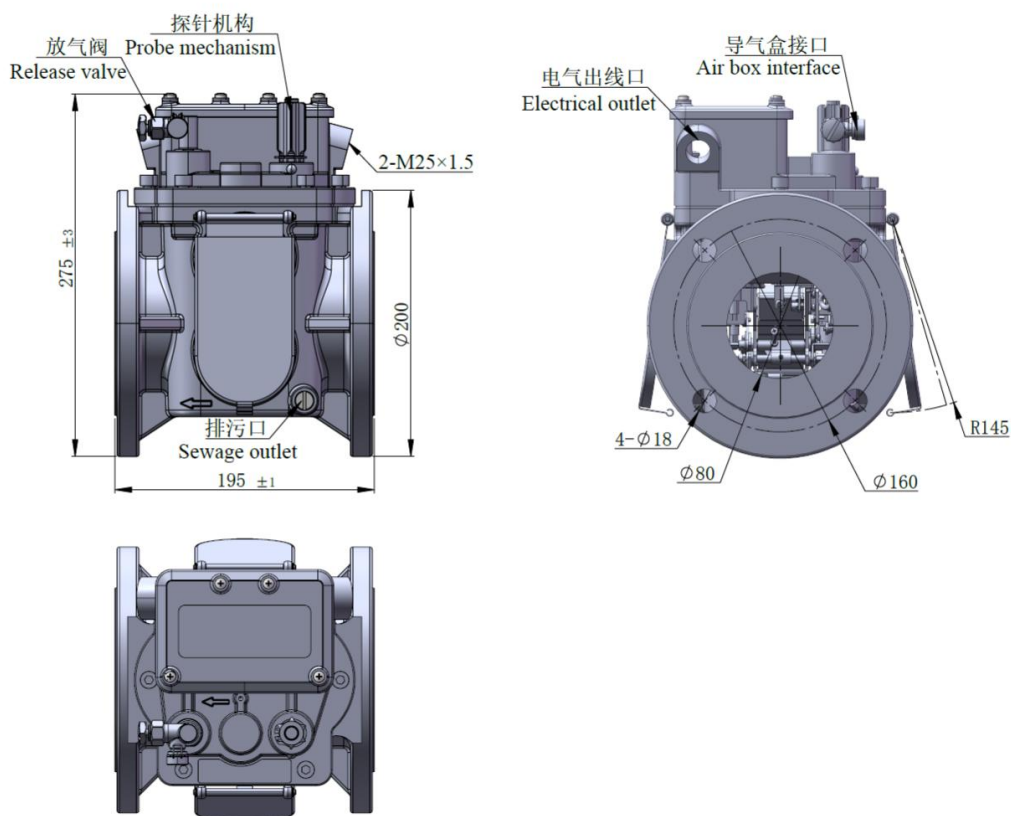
QJ9-80TH-03 气体继电器（圆法兰）外形尺寸
